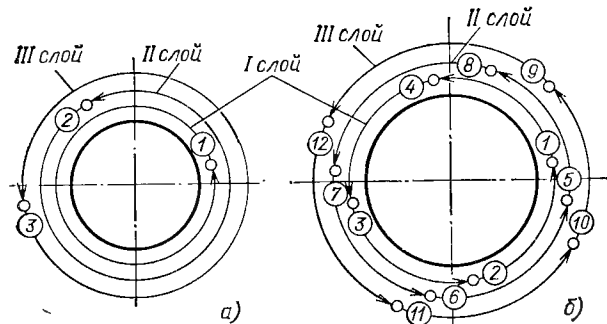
Порядок наложения слоев (валиков) при сварке горизонтального стыка труб одним сварщиком.
